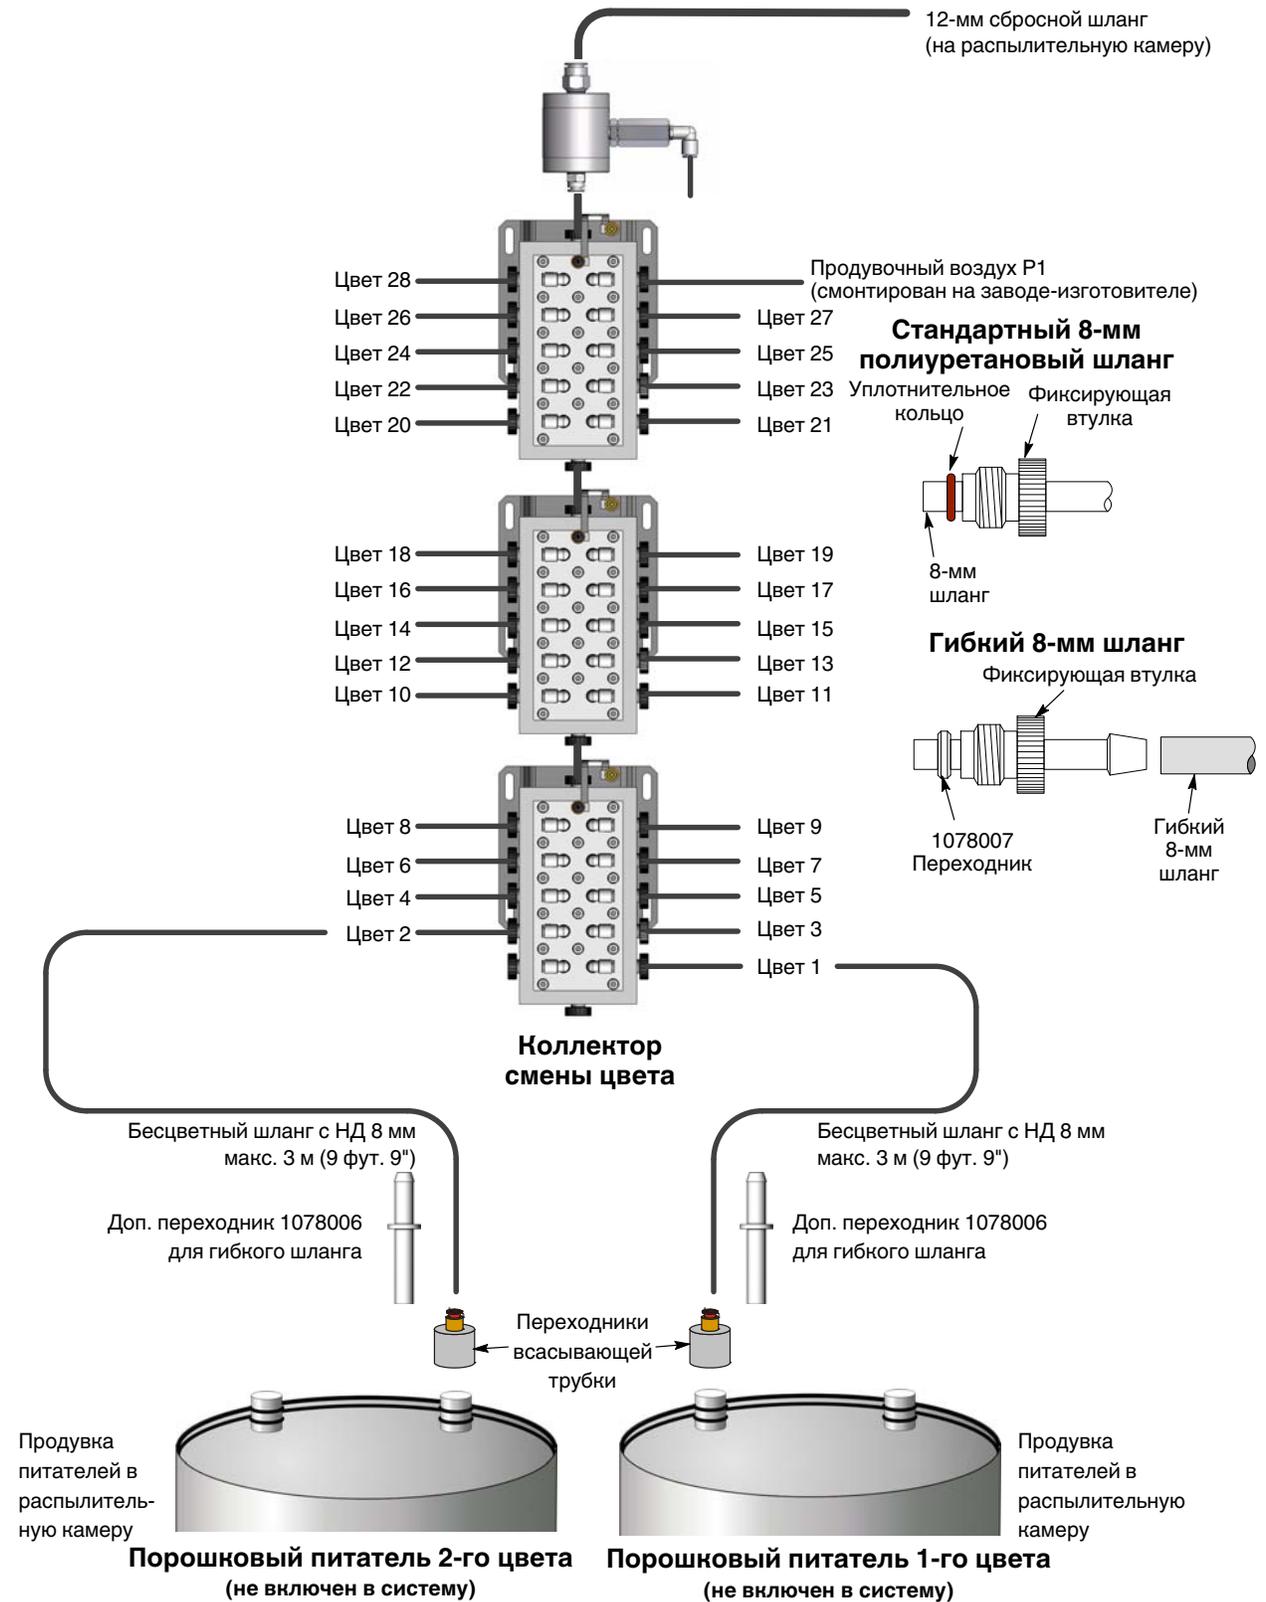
Монтаж всасывающего и сбросного шлангов
